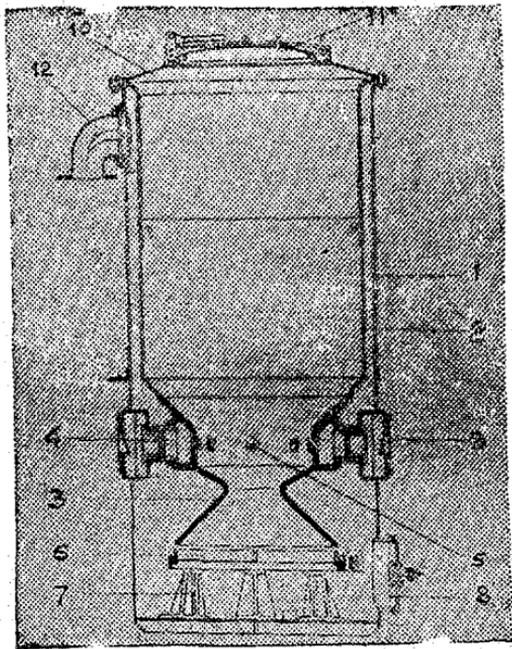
Газогенератор в сборе: 1—корпус газогенератора; 2—бункер газогенератора; 3—камера газификации (горения) газогенератора; 4—фурторки газогенератора; 5—фурмы камеры горения; 6—колосниковая решетка; 7—опора колосниковой решетки, 8—зольниковый люк; 9—воздушные клапаны; 10—крышка газогенератора; 11—загрузочный люк газогенератора; 12—патрубок отбора газа.
